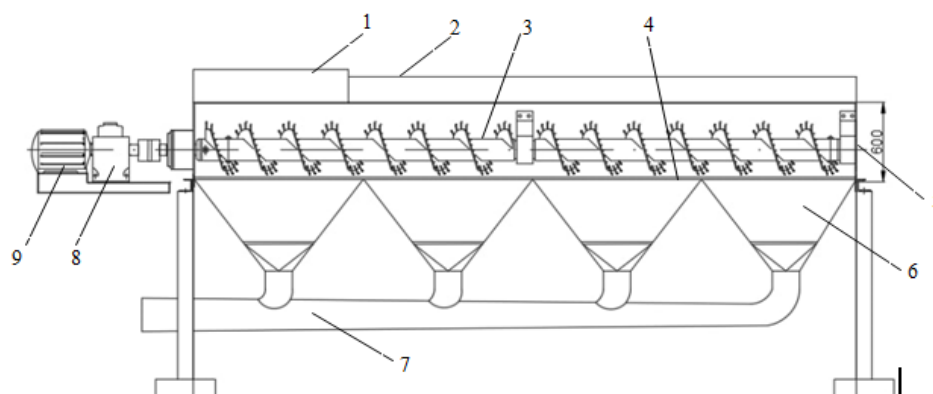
Схема усовершенствованного устройства для транспортировки и очистки хлопка
